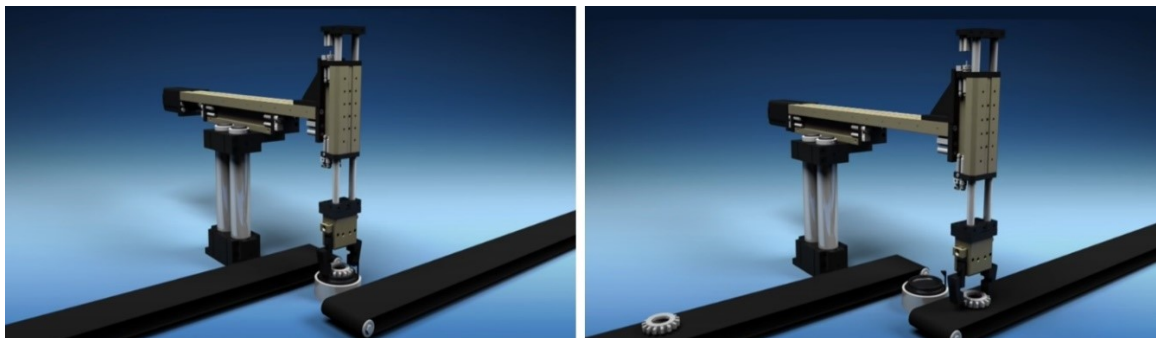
Přivedení objektu manipulace pomocí dopravníku a uchopení předmětu manipulátorem [25]
